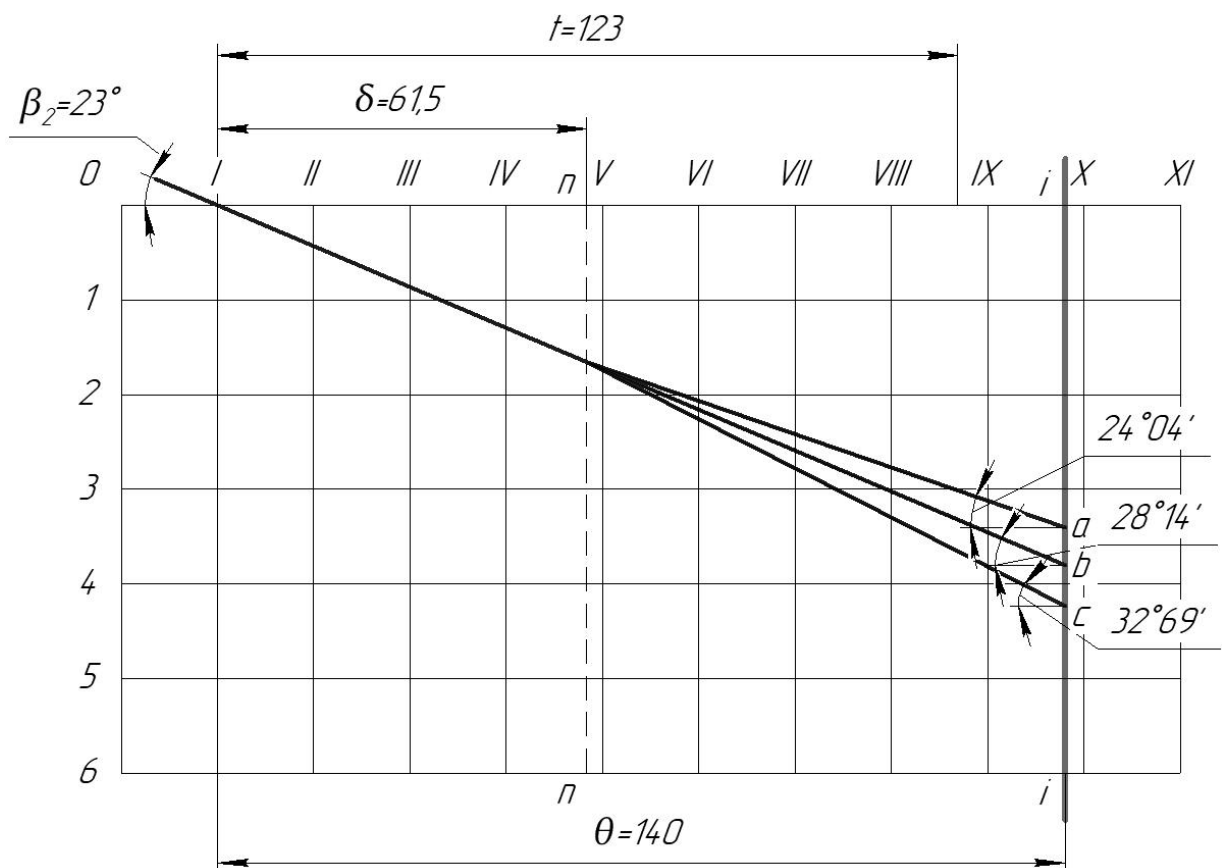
Профілювання поверхні лопаті на розгортці циліндра
